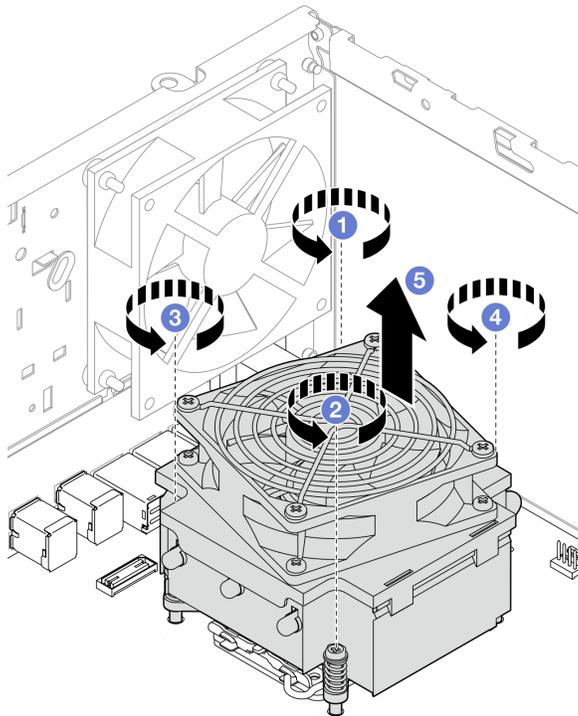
Desserrage des vis du module dissipateur thermique et ventilateur pour les processeurs avec une enveloppe thermique inférieure à 95 W
